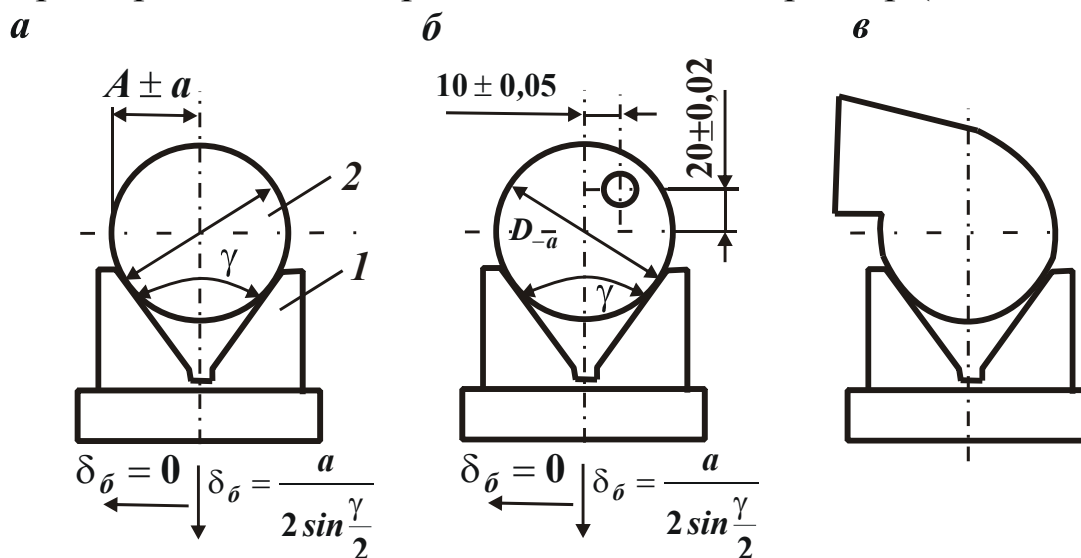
Схема базирования заготовки с главной базой, имеющей вид цилиндрической наружной поверхности, на призму.
